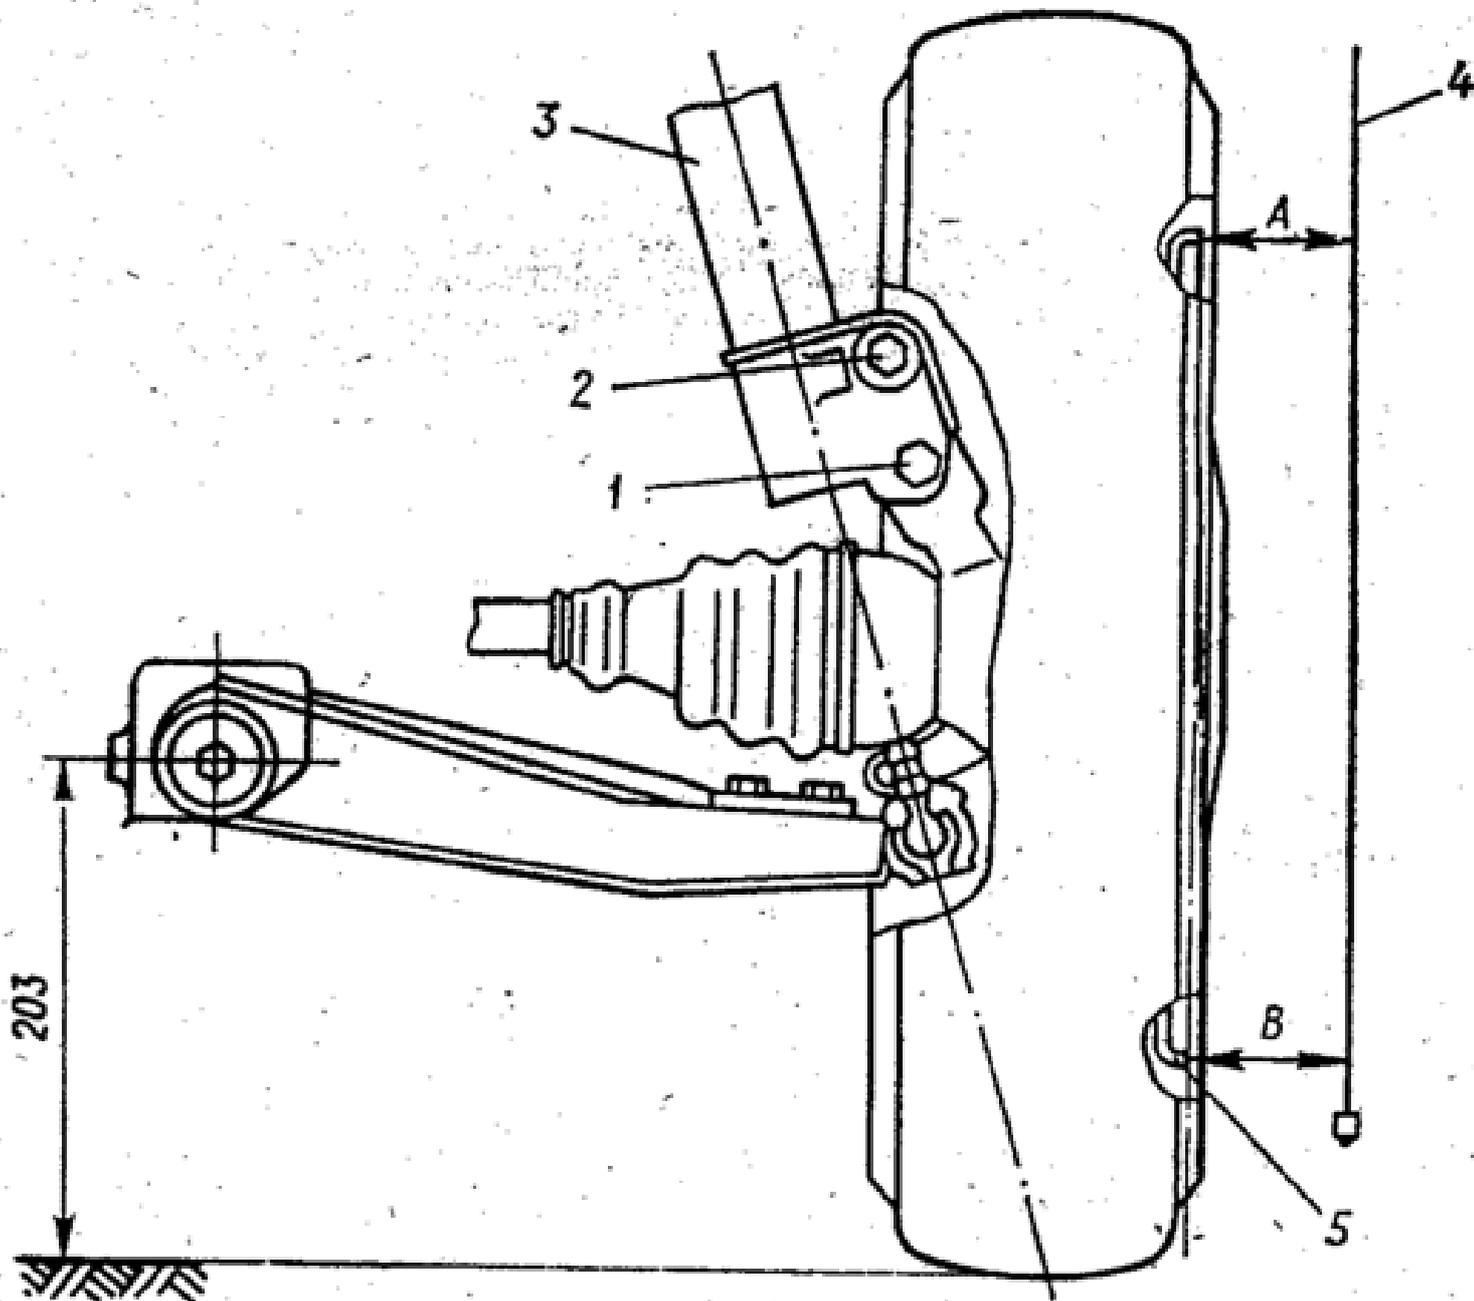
Проверка и регулировка угла развала переднего колеса: 1 - болт крепления стойки к поворотному кулаку; 2 - болт регулировки угла развала и крепления стойки к поворотному кулаку; 3 - амортизационная стойка; 4 - шнур отвеса; 5 - диск колеса
